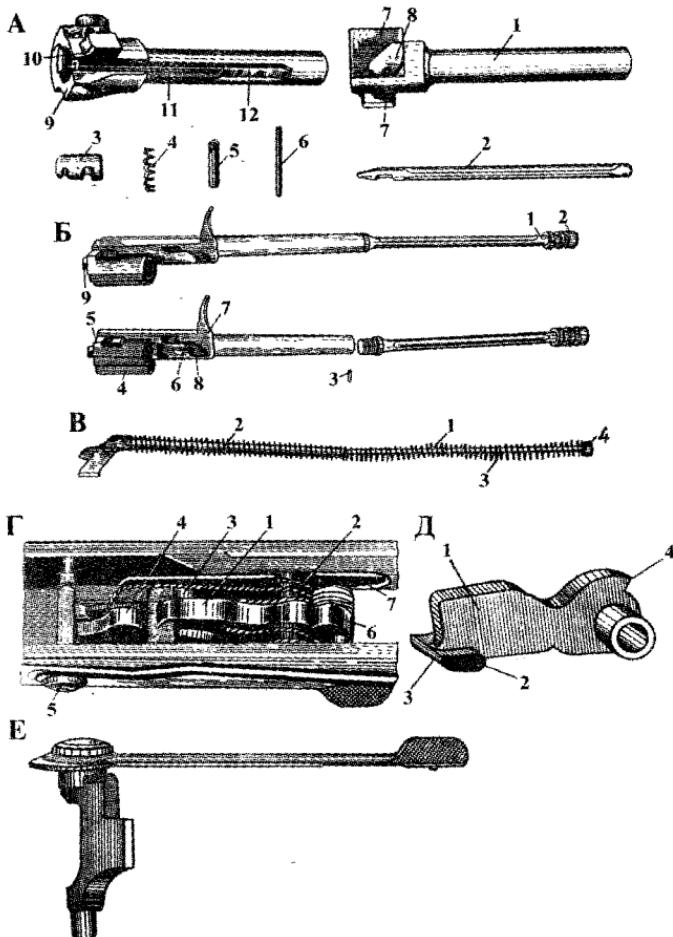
Детали и узлы автомата Калашникова АК-47: А - затвор в собранном и разобранном виде: 1 - остиб затвора; 2 - ударник; 3 - выбрасыватель; 4 - пружина выбрасывателя; 5 - ось выбрасывателя; 6 - шпилька ударника; 7 - боевые выступы; 8 - ведущий выступ; 9 - досыпатель; 10 - скос; 11 - продольный паз; 12 - выемка. Б - затворная рама в собранном виде: 1 - сток; 2 - поршень; 3 - штифт; 4 - прилив; 5 - выступ; 6 - запирающий скос; 7 - отпирающий скос; 8 - задняя прямая стенка; 9 - выступ. В - возвратный механизм в собранном виде: 1 - возвратная пружина; 2 - направляющая трубка; 3 - шайба. Г - ударно-спусковой механизм: 1 - курок; 2 - боевая пружина; 3 - спусковой крючок; 4 - шептalo одиночного огня; 5 - переводчик; 6 - автоспуск; 7 - пружина автоспуска. Д - курок: 1 - головка; 2 - боевой взвод; 3 - взвод одиночного огня; 4 - взвод автоспуска. Е - переводчик-предохранитель.
